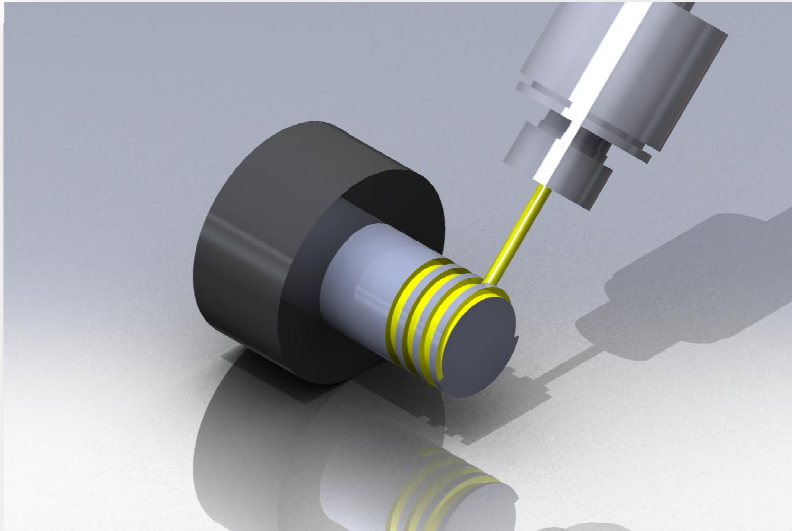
Fräsen einer Wendel auf der Mantelfläche
